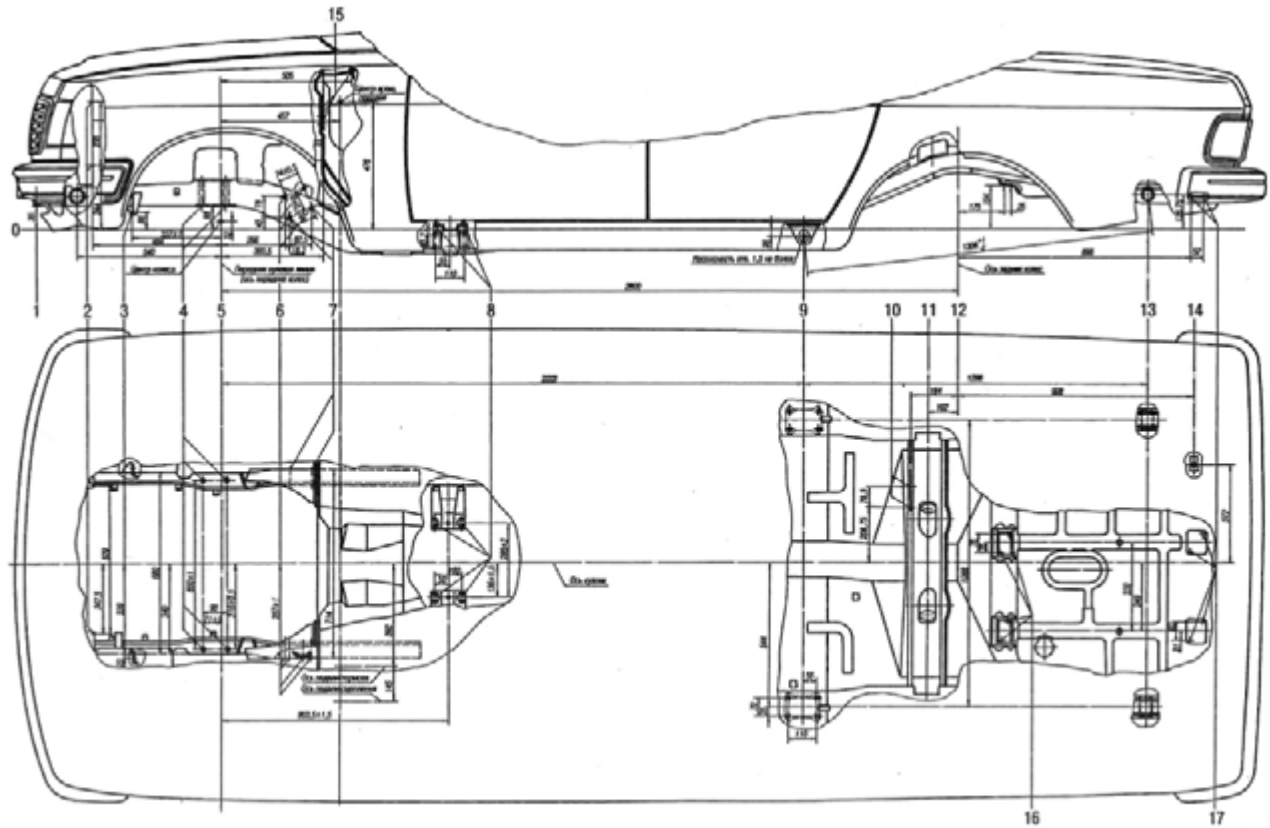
Контрольно-установочные размеры крепления агрегатов:
